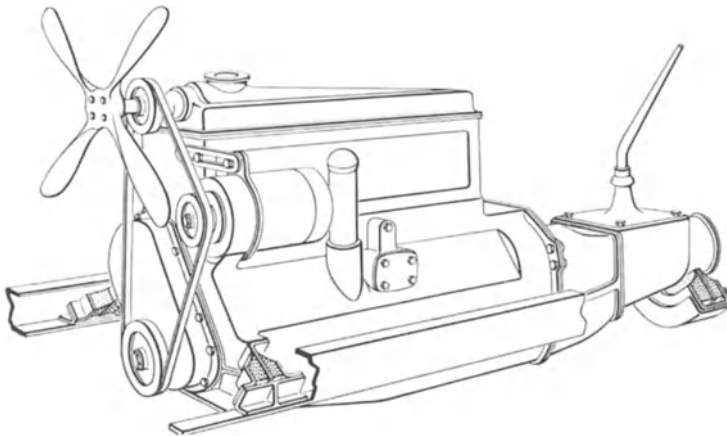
Elastische Lagerung eines Kraftwagenmotors mit schubbeanspruchten Gummifedern.
